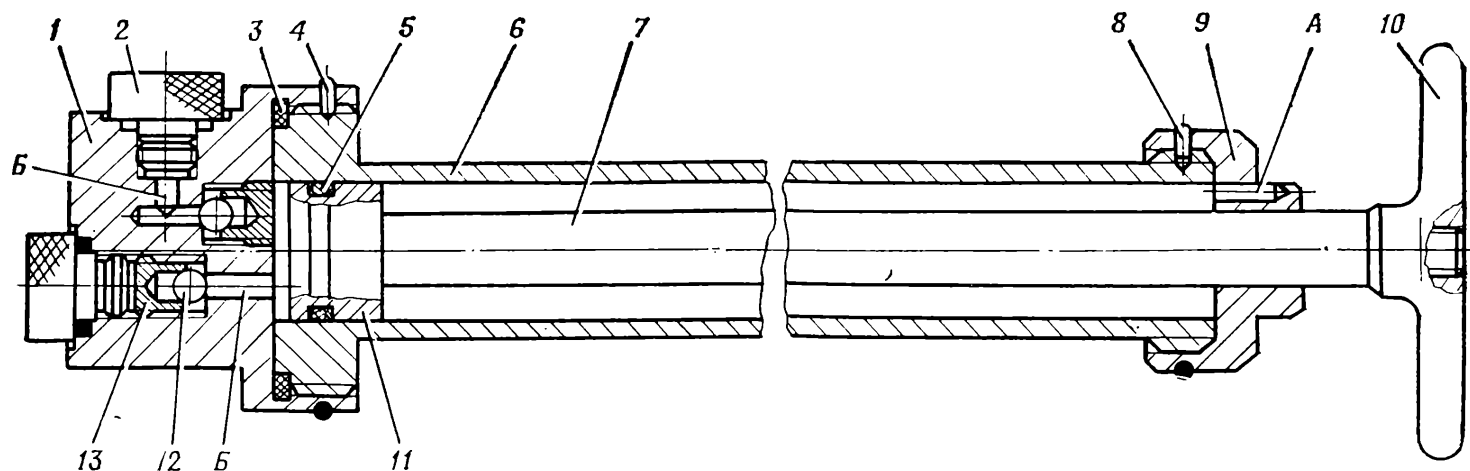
Приспособление 41.240 для заливки жидкости в тормоз отката:
